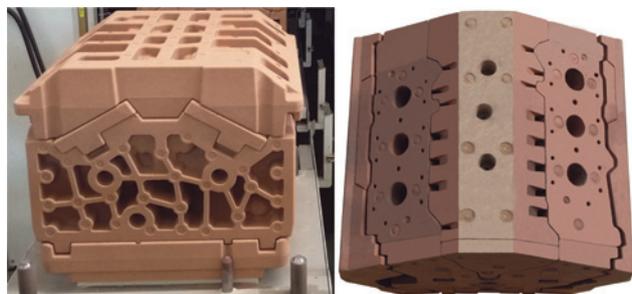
Примеры стержневых пакетов для получения алюминиевых отливок V8- (слева) и V6- (справа) блоков двигателей легковых машин методом «пакетной формовки» [3]
